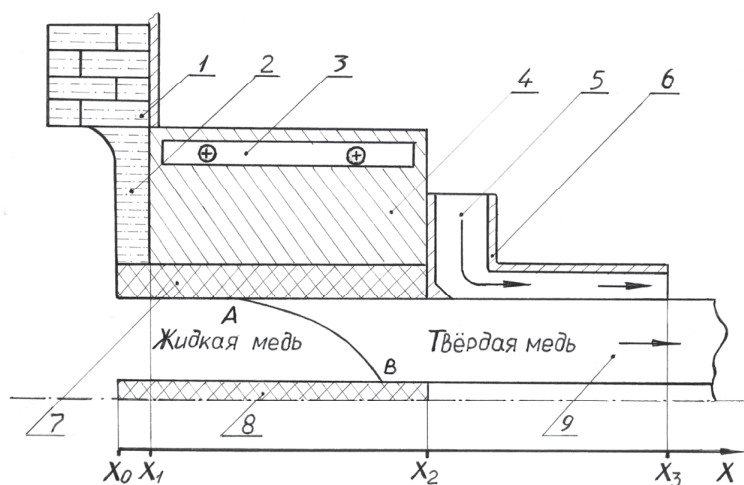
Схема медно-графитового кристаллизатора для литья медных трубных заготовок
